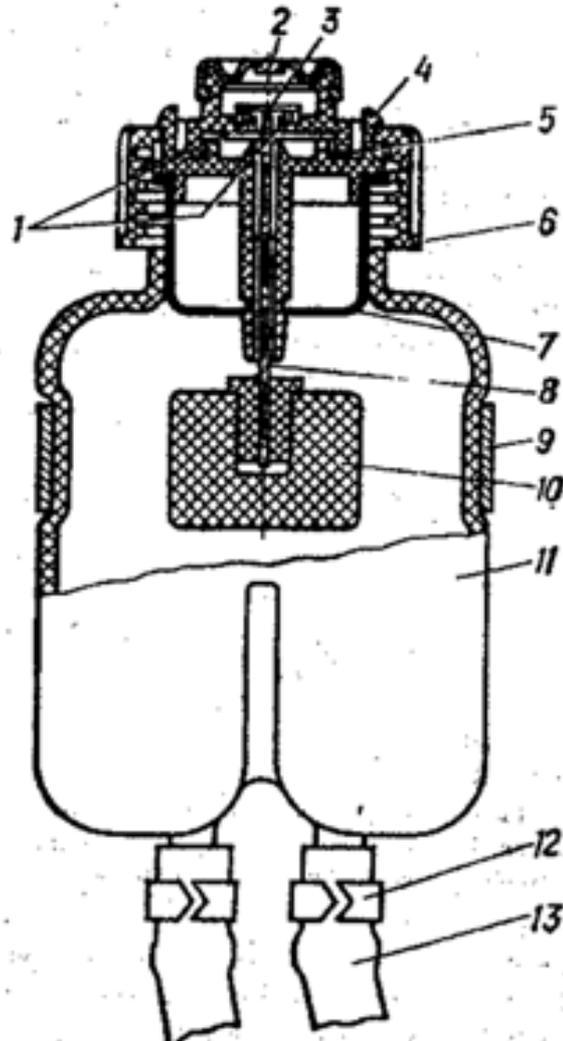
Бачок тормоза и датчик аварийного уровня тормозной жидкости: 1 - неподвижный контакт; 2 - защитный колпачок; 3 - подвижный контакт; 4 - основание датчика; 5 - уплотнительное кольцо; 6 - крышка бачка; 7 - отражатель; 8 - толкатель; 9 - хомут крепления бачка; 10 - поплавок; 11 - бачок; 12 - хомут; 13 - шланг.
